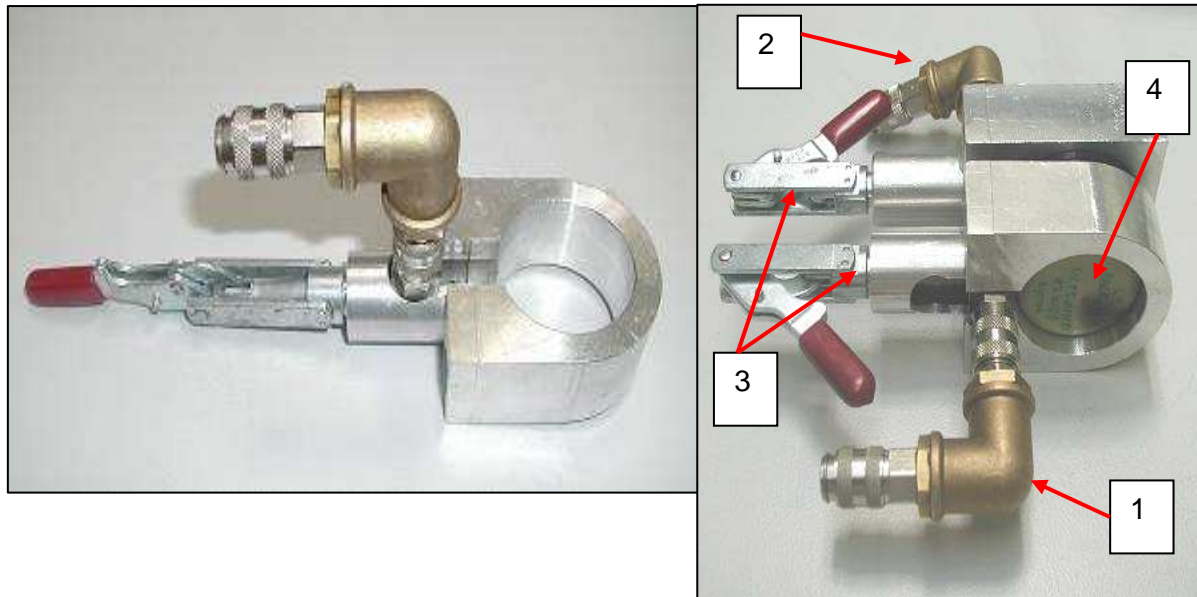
Horní (A) a dolní (B) svařovací přípravek
